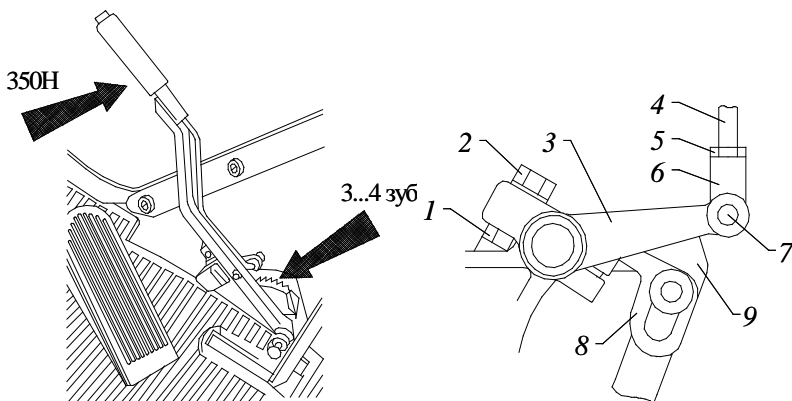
Схема проверки и регулировки стояночного тормоза:
